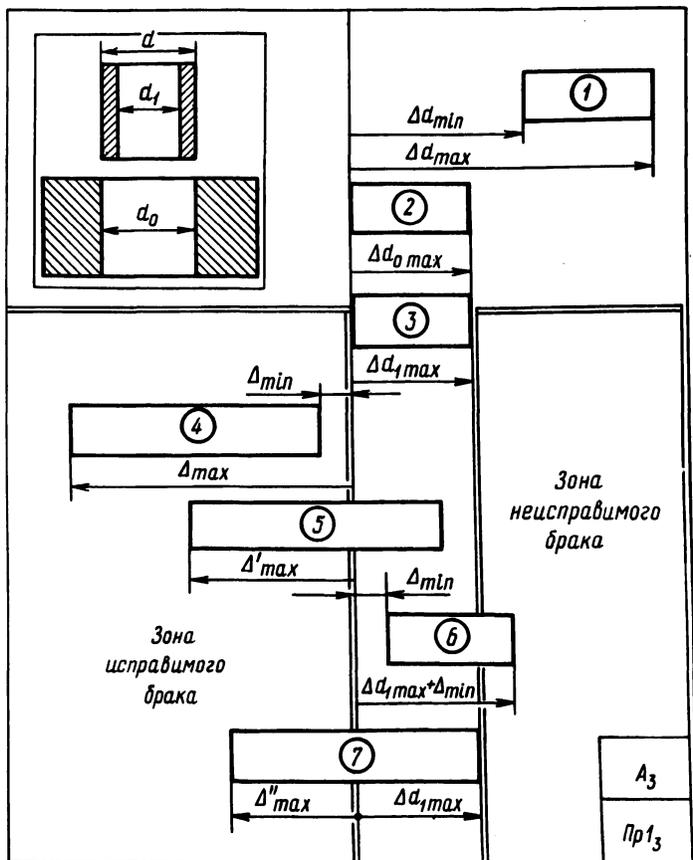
Схема расположения полей допусков размеров поверхностей деталей в партии сопряжений
